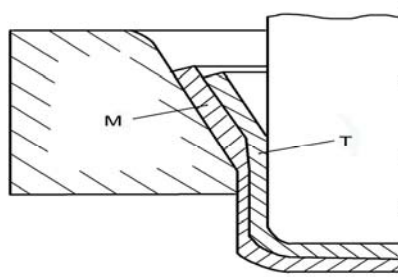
Схема комбинированной вытяжки двухслойной заготовки:
